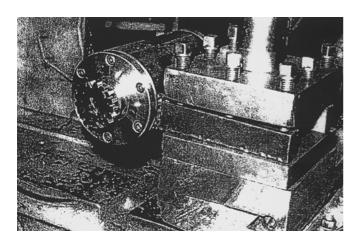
Установка накатного шпинделя с накатным инструментом в резцедержатель токарного станка
